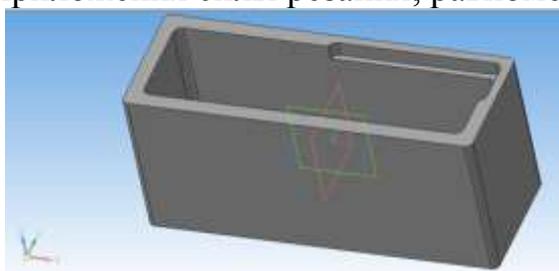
3D-модель корпусной детали с нежесткими стенкам
